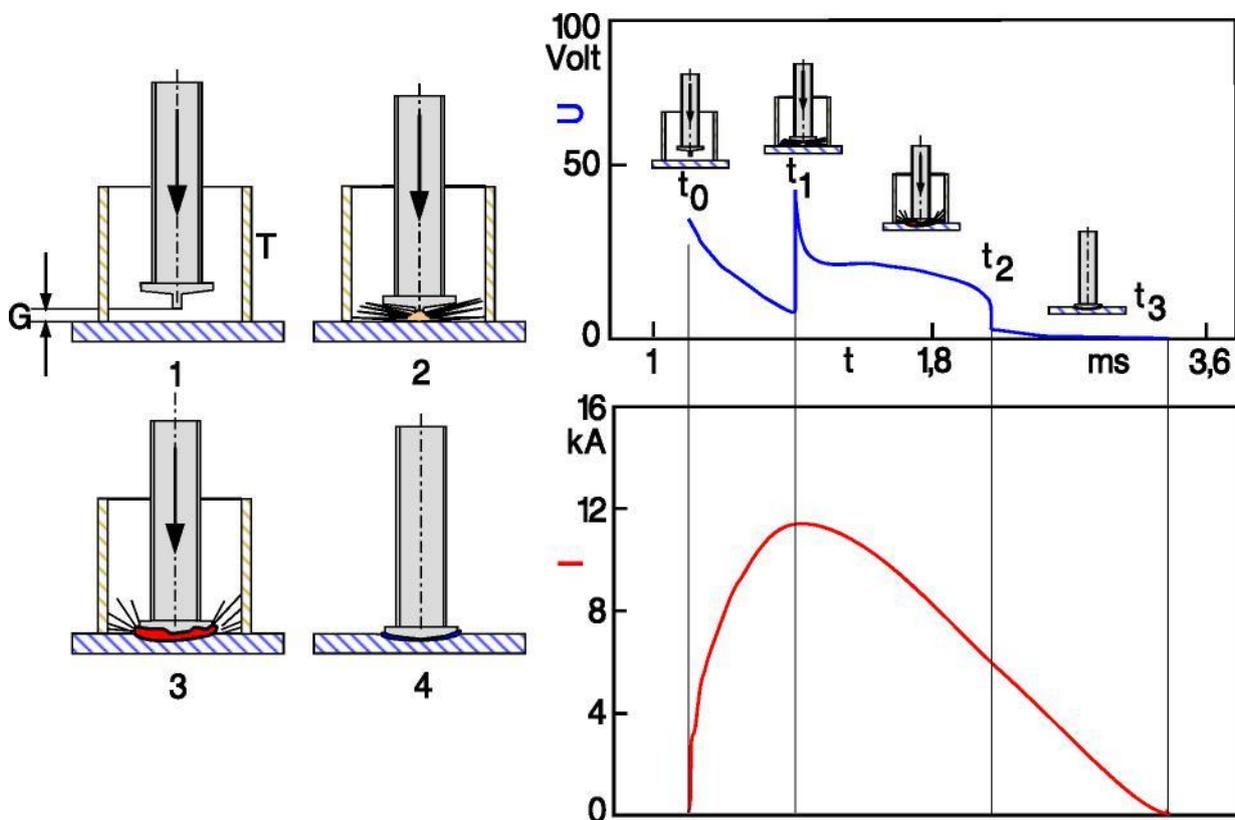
Arbeitsablauf mit Spannung und Strom beim Bolzenschweißen mit Spitzenzündung (Spaltverfahren)
